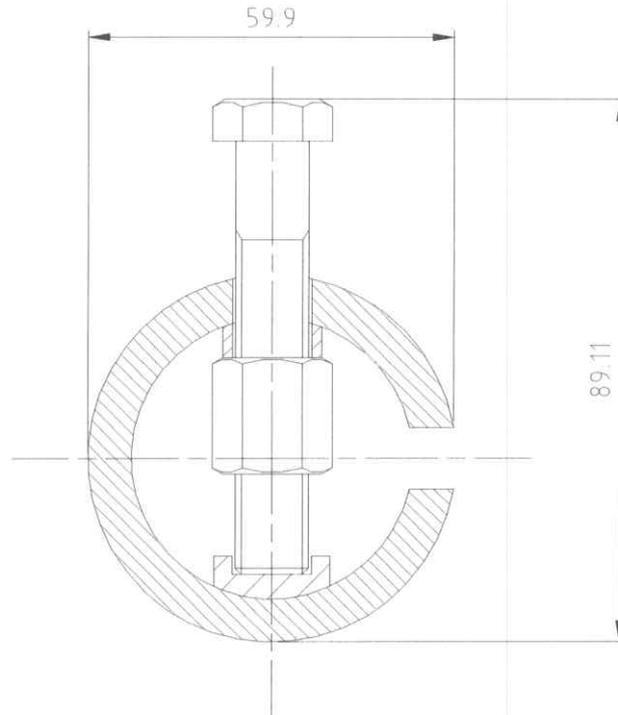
С-образный образец с винтовым нагружающим механизмом
